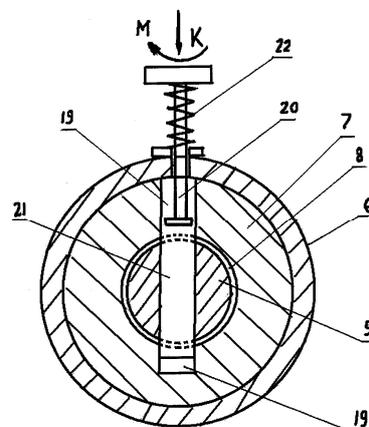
Укрупненный вид пальца фиксатора штока тормозного цилиндра
